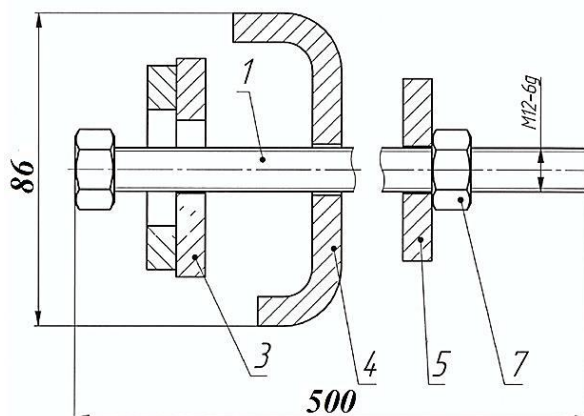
Болт из набора «СНKL-3 ССД» с крепёжными деталями:
